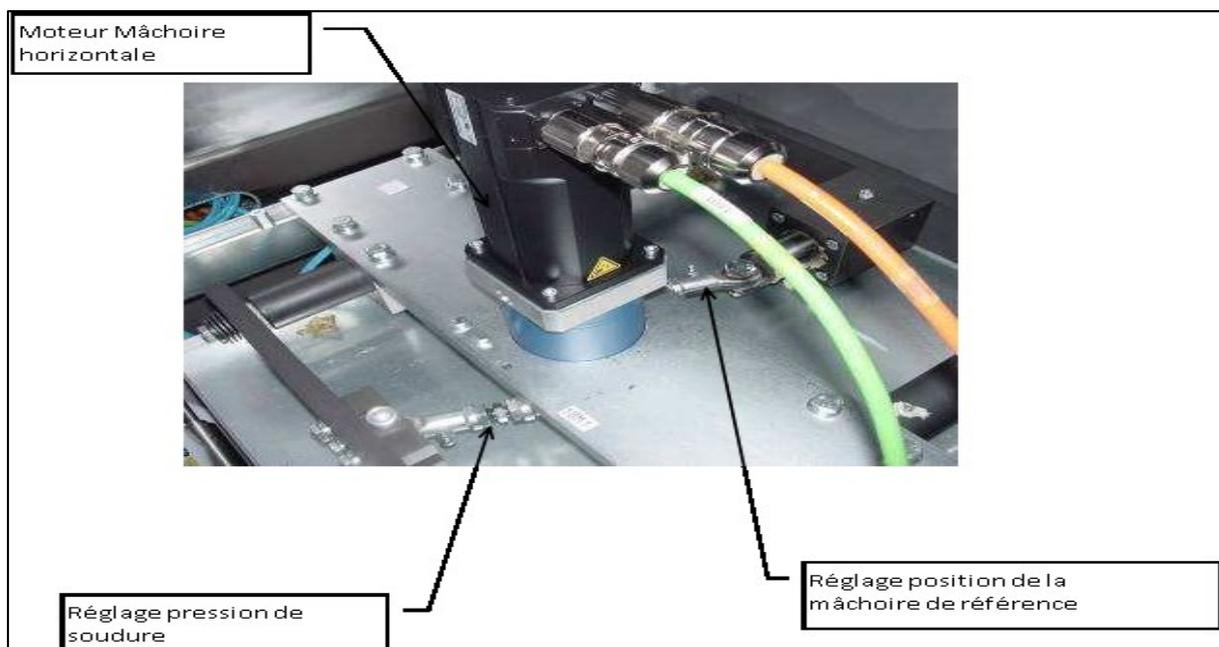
moteur pour le système de soudure horizontale.
